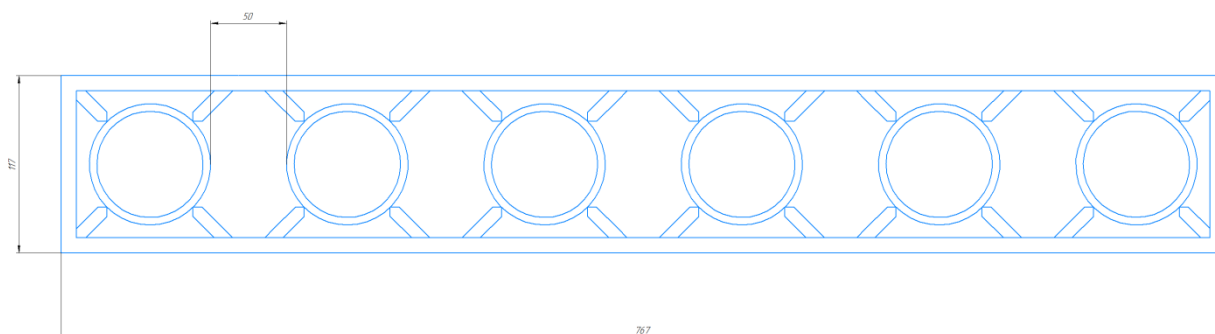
Верхня проекція схеми розташування на підвісному пристрої
